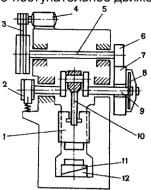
Кинематическая схема горячештамповочного кривошипного пресса
